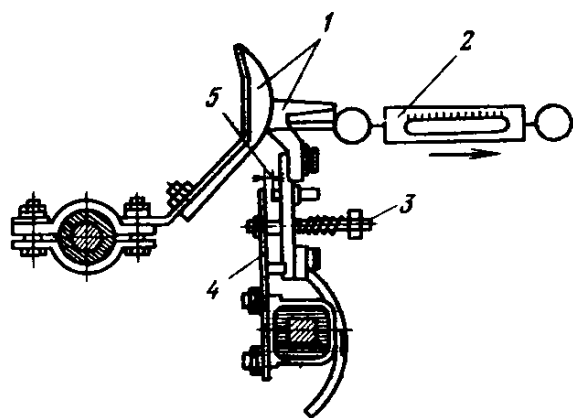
Камера дуго-гашения контактора КВМ реверсоров РВМ:
